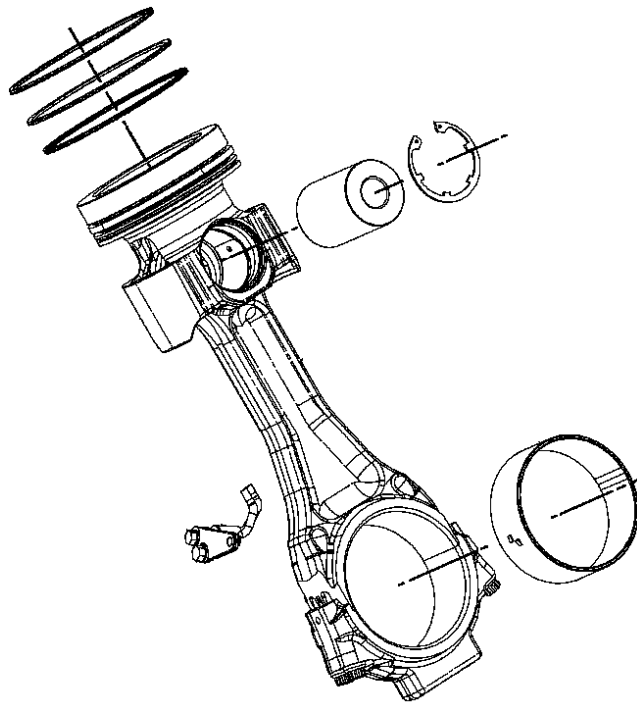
Поршень, поршневий палець, шатун та шатунний підшипник дизеля Cat 3516 [3]
